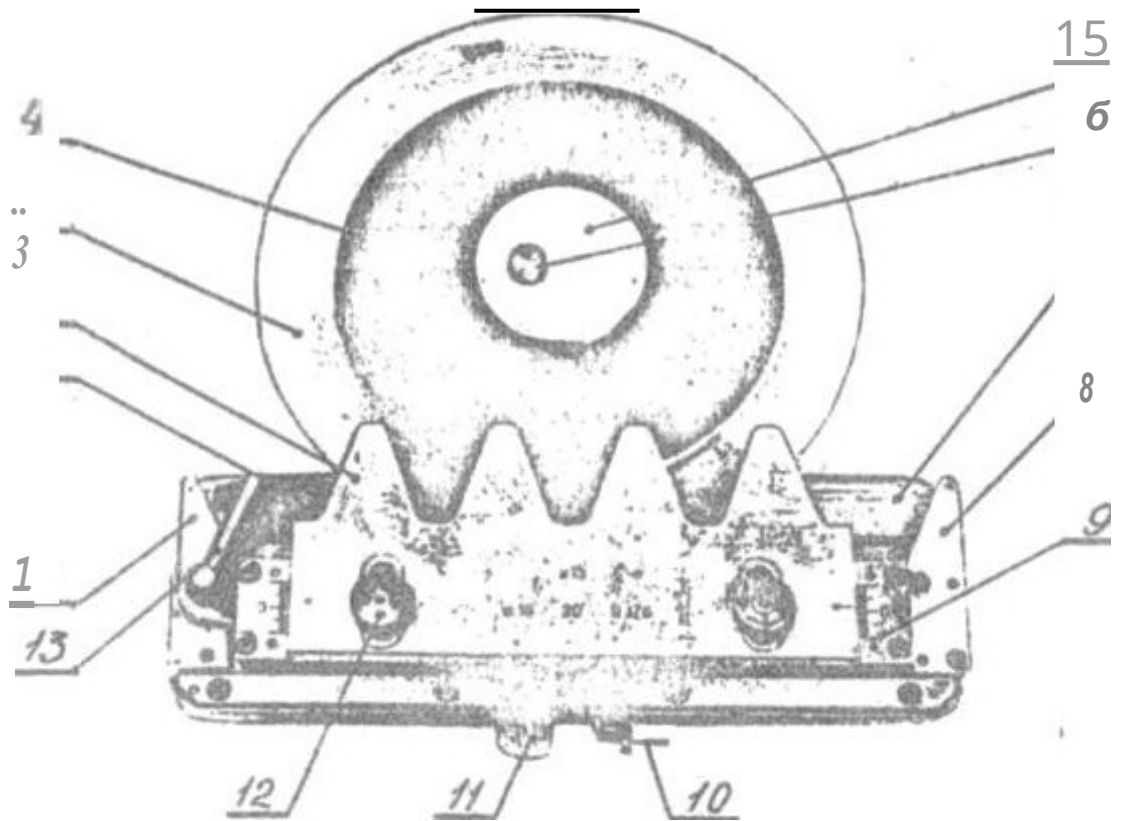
Прибор для вычерчивания эвольвентных профилей зубьев методом обкатки
